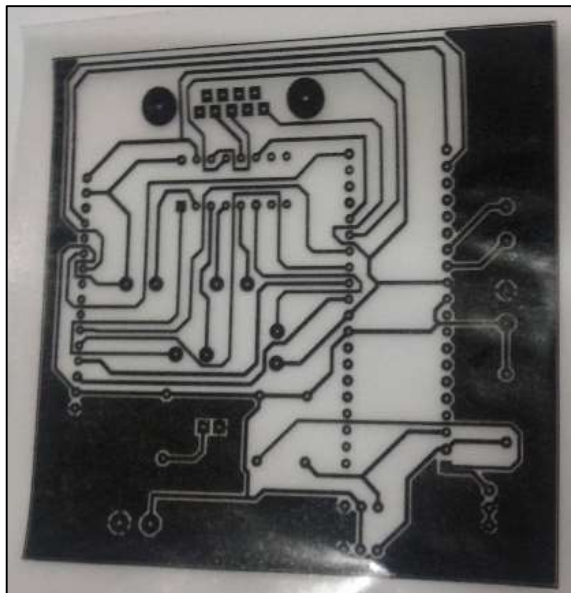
Impreso del diseño de la pista para la PCB de la tarjeta meteorológica, para la adquisición de datos.
